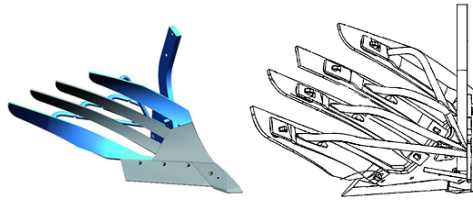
Пластинчатые корпуса фирмы «Lemken»:
